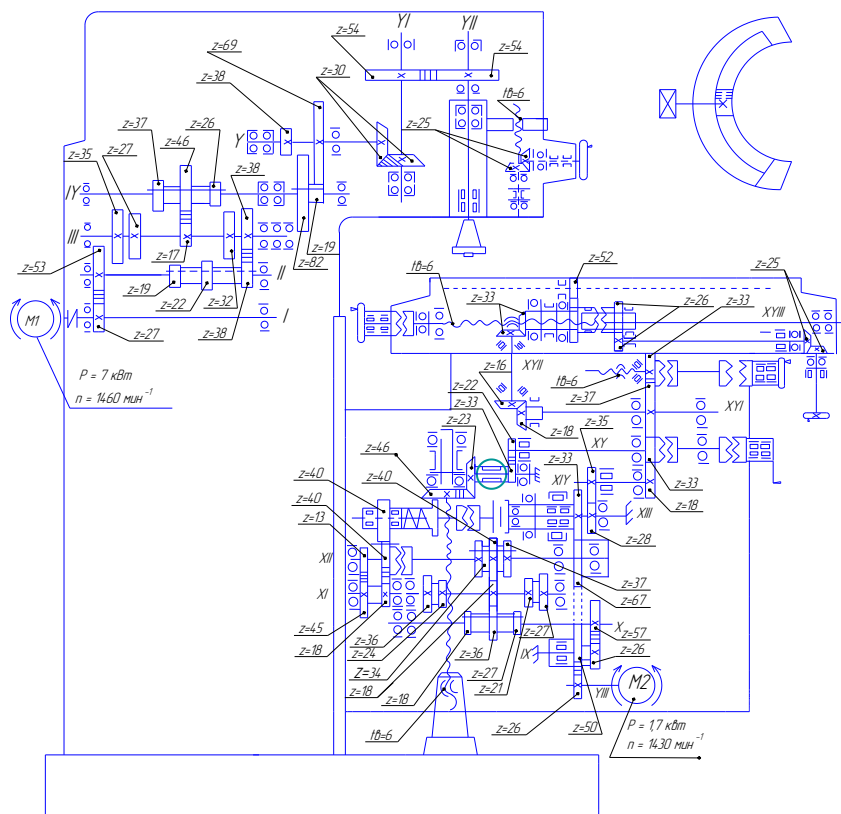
Кинематическая схема станка мод. 6Л12П
